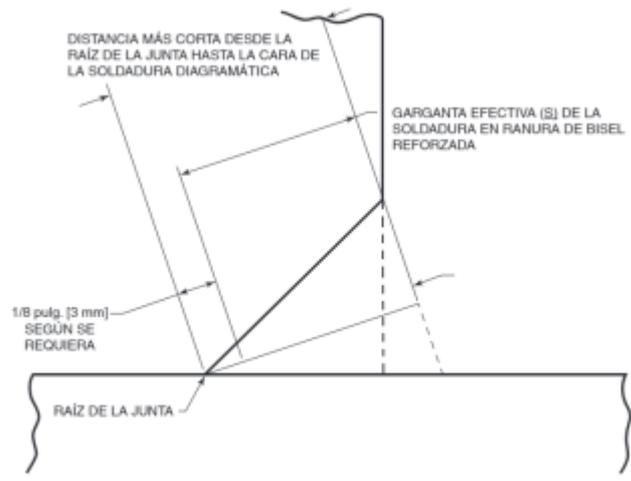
Soldadura en ranura de bisel con soldadura en filete reforzada (ver 4.4.2.7)
